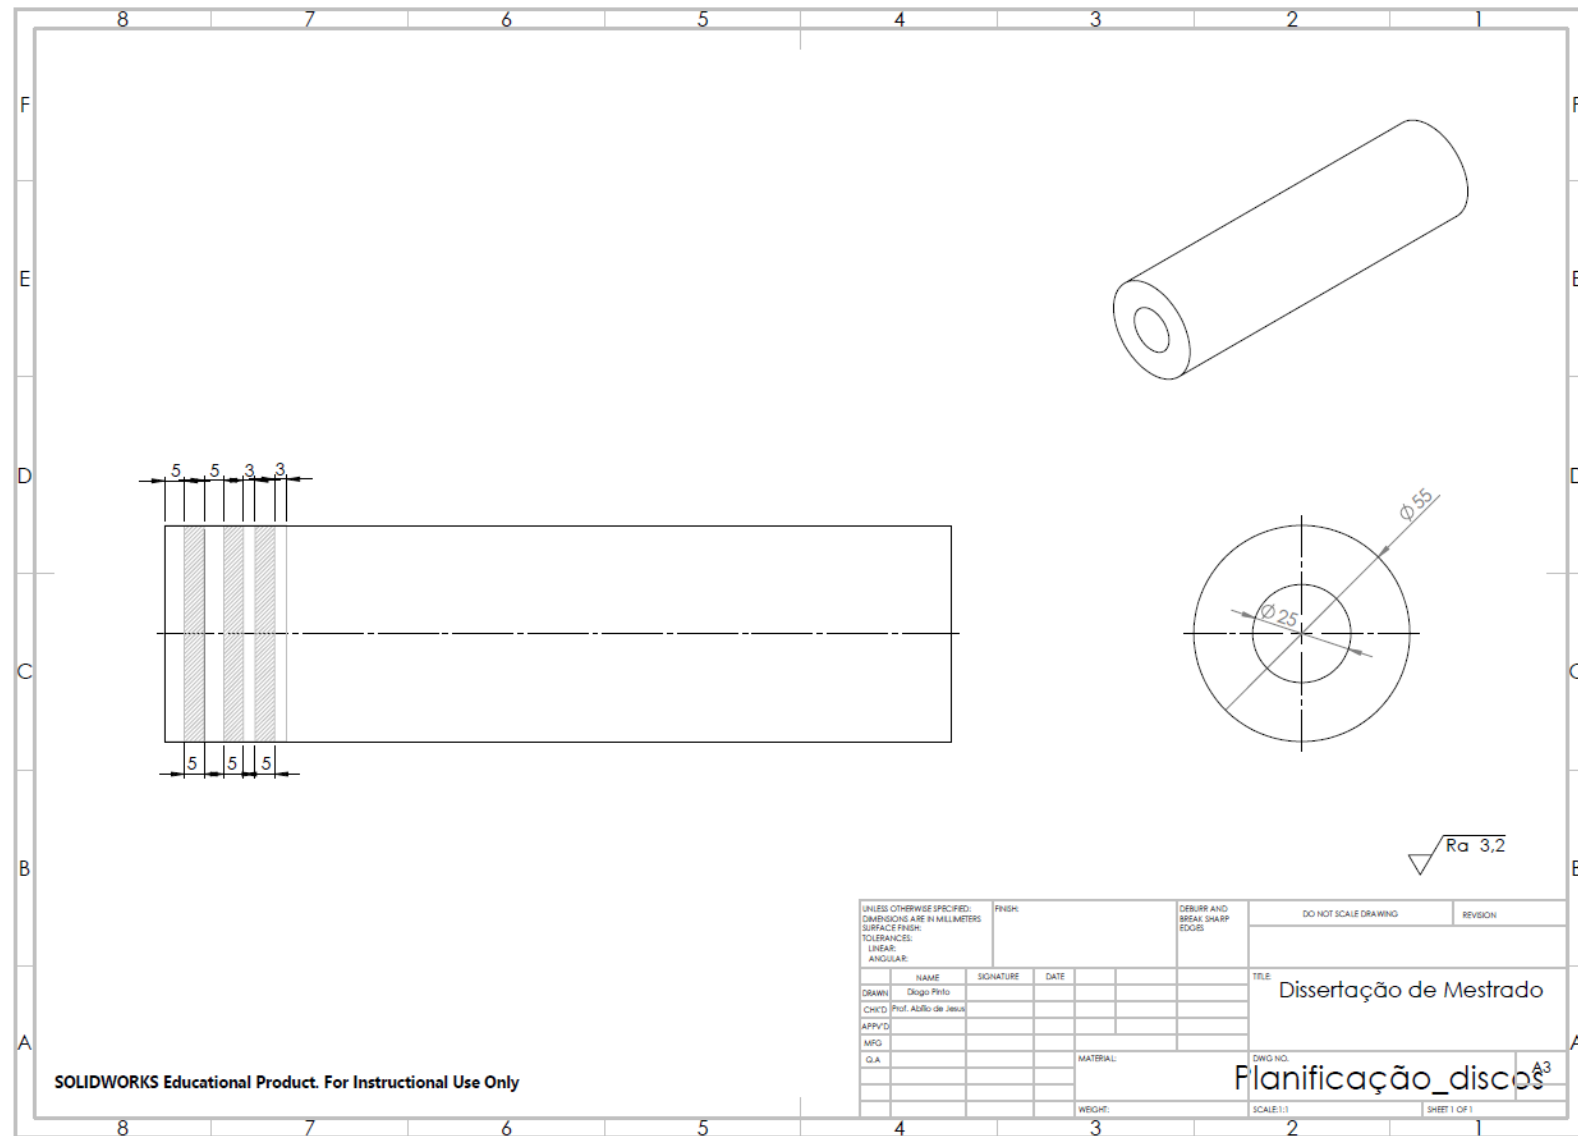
Planificação para corte dos provetes para ensaio de arrombamento
